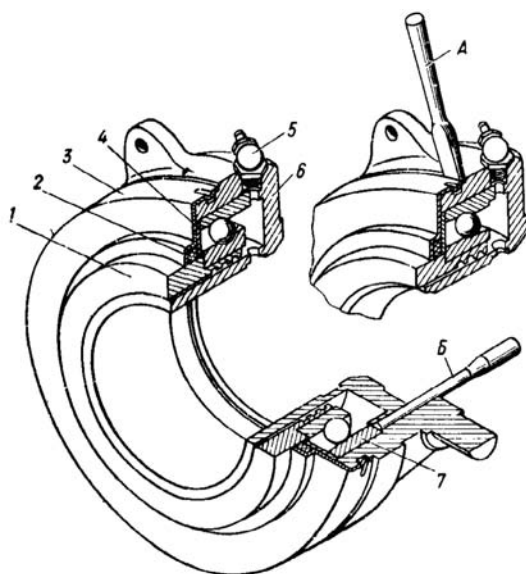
Разборка выжимного подшипника: 1 — упор выжимного подшипника; 2 — сальник; 3 — крышка; 4 — шайба; 5 — масленка; 6 — корпус; 7 — подшипник; А — лопатка монтажная; Б — наставка
